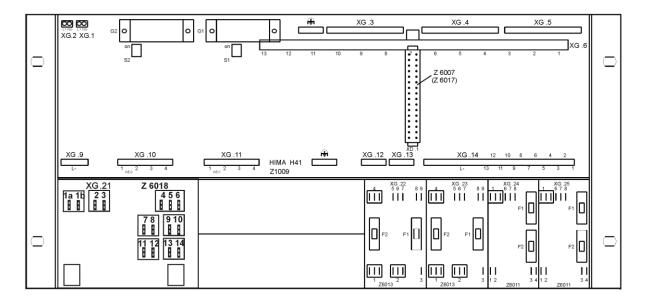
Anschlüsse auf der Rückseite des System-Baugruppenträgers K 1409
